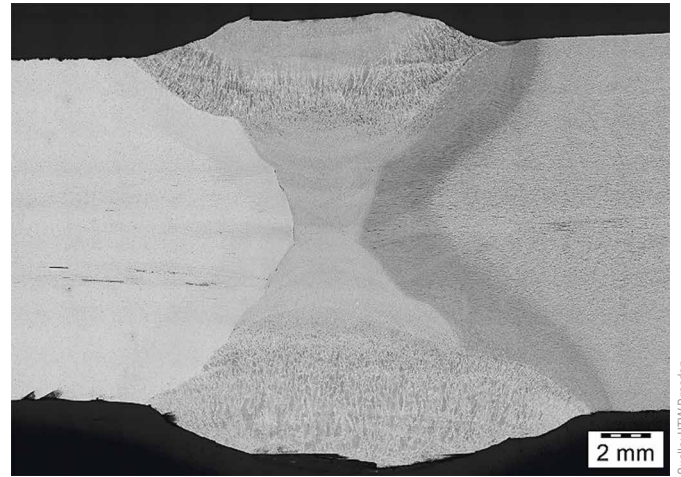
Geätzter Makroschliff einer Schweißprobe des Materials AV
